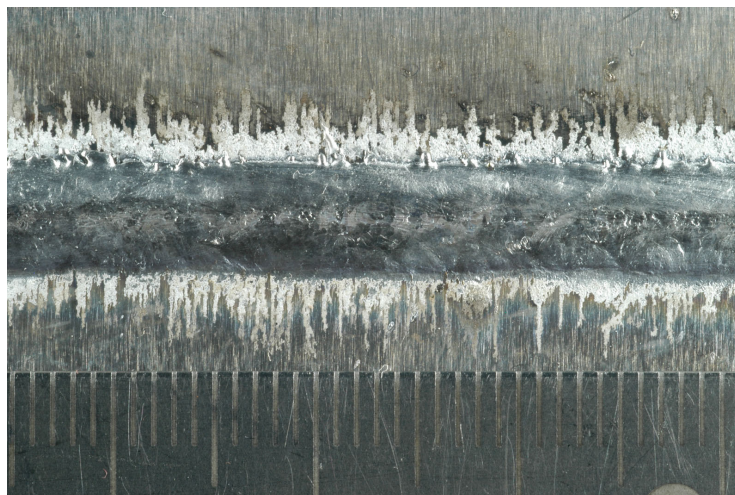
Soldagem de chapas de alumínio. Espessura: 2 mm. Arame: AISi5, 1,2 mm de diâmetro. Velocidade de soldagem: 2,7 m/min. Demais parâmetros: Tabela 7.1.
